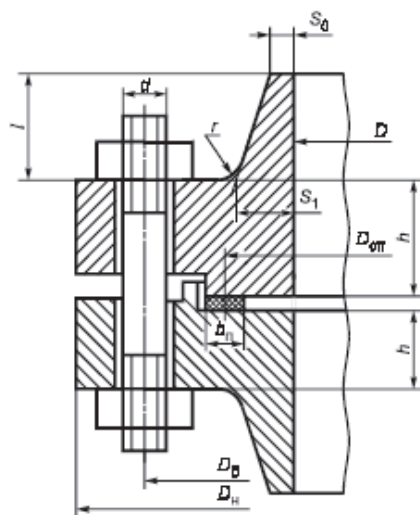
Фланцевое соединение с уплотнительной поверхностью типа выступ — впадина
